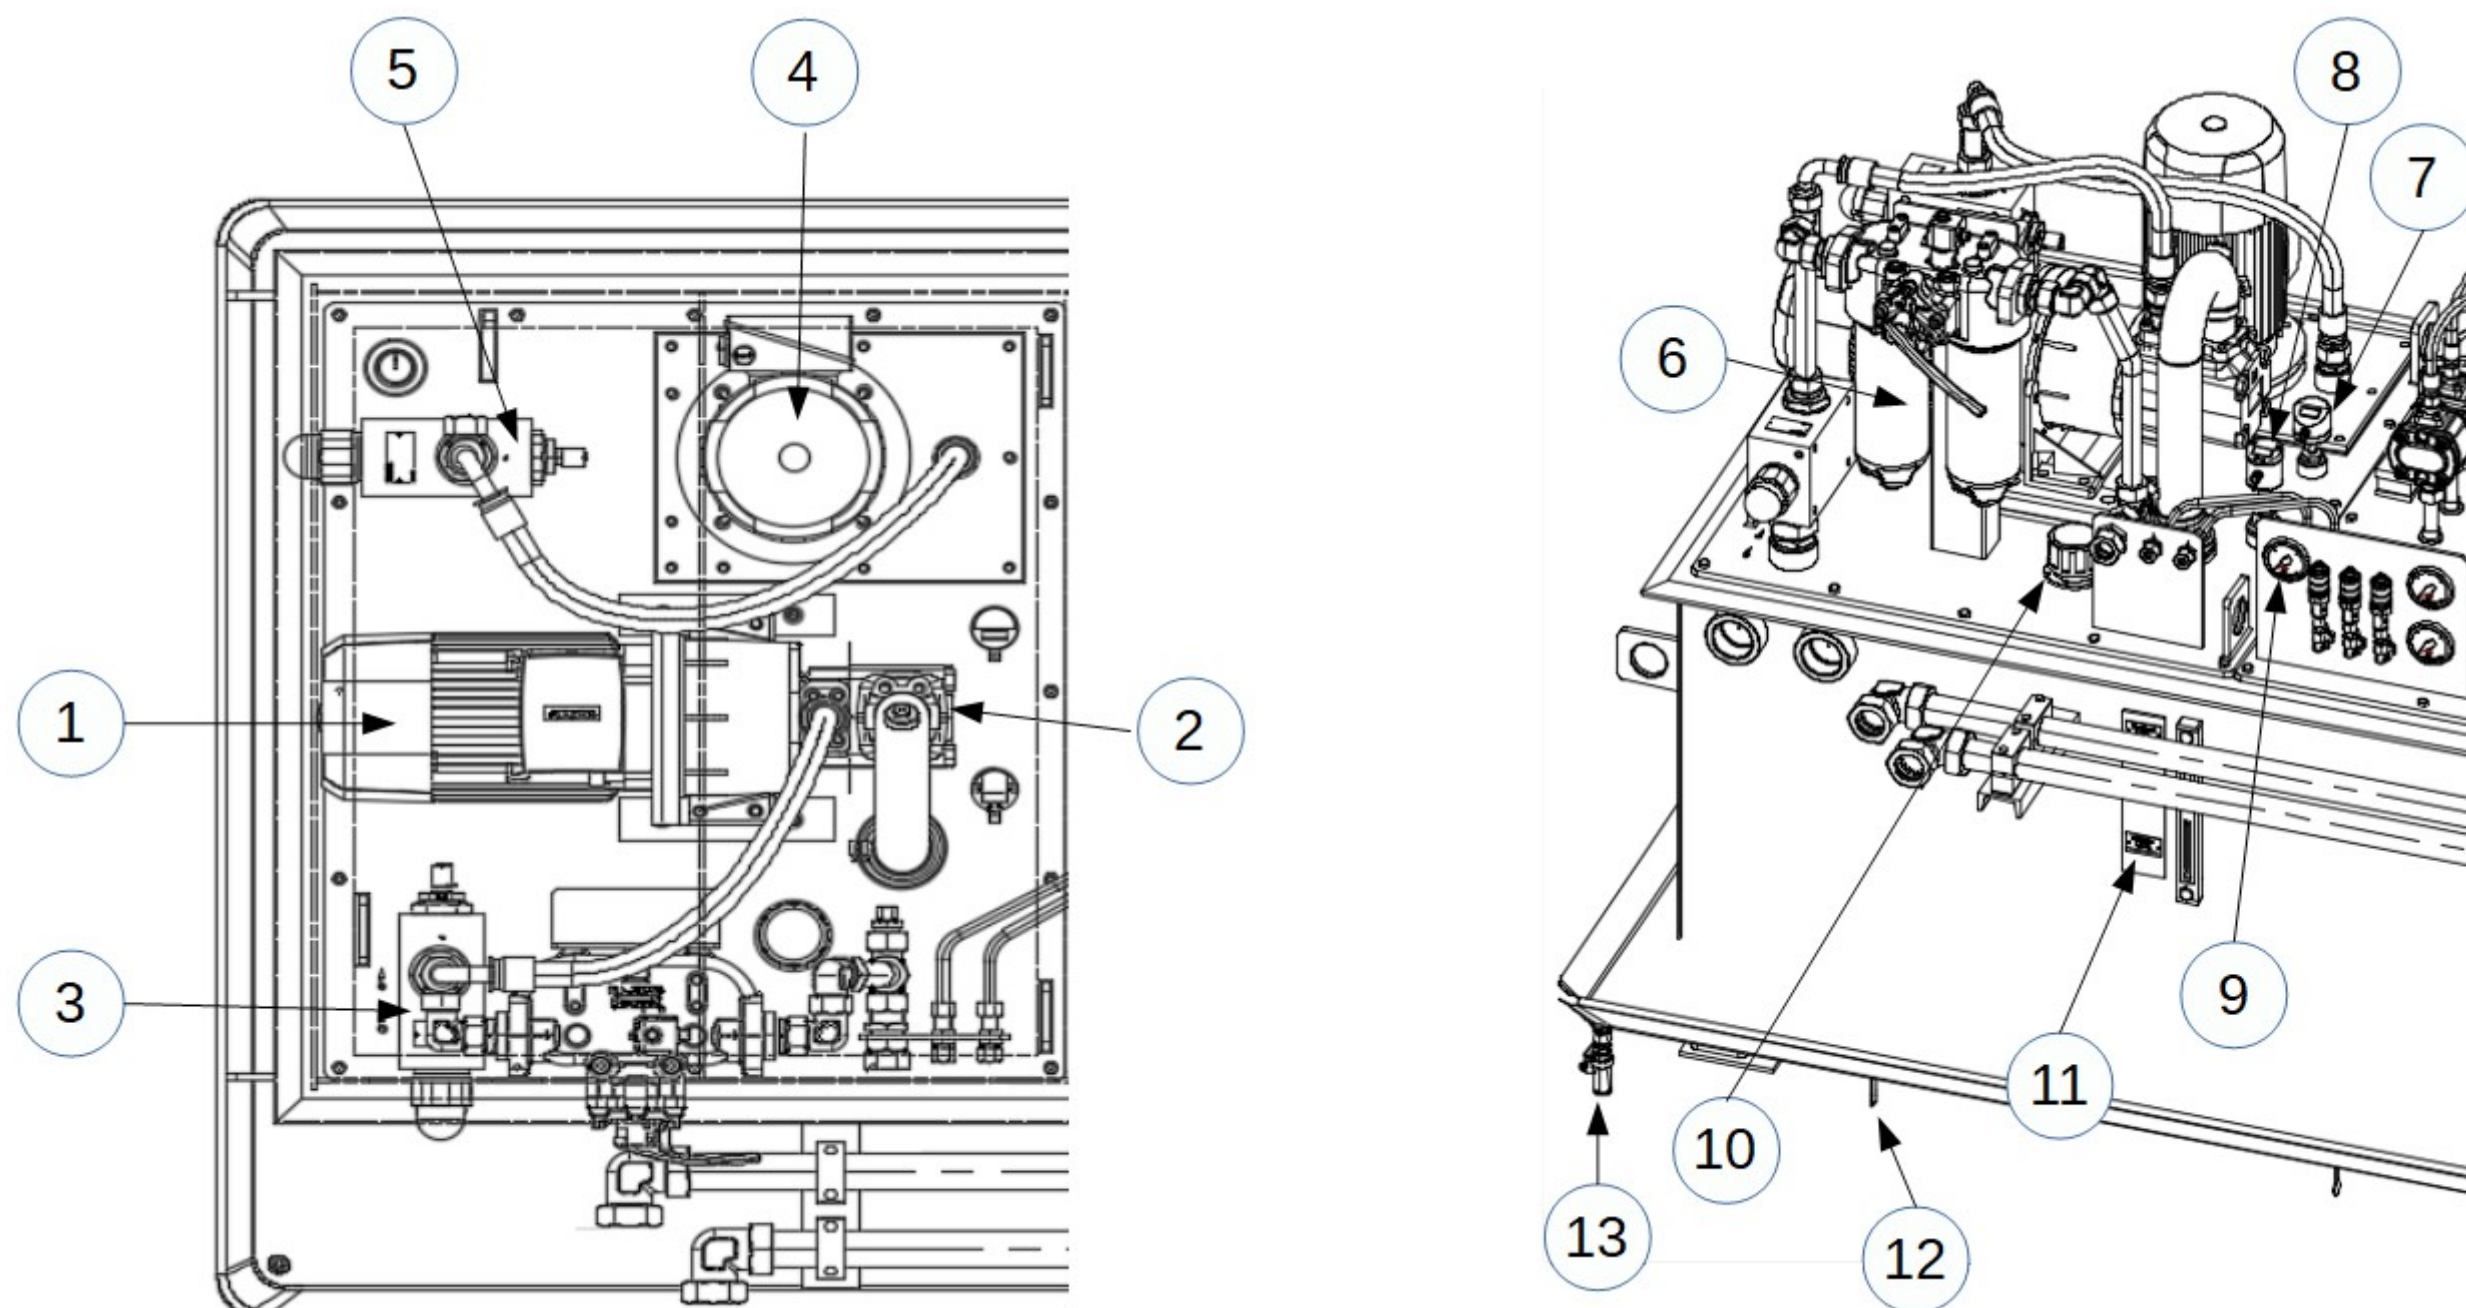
Блок смазки передней бабки. Детальный вид.
